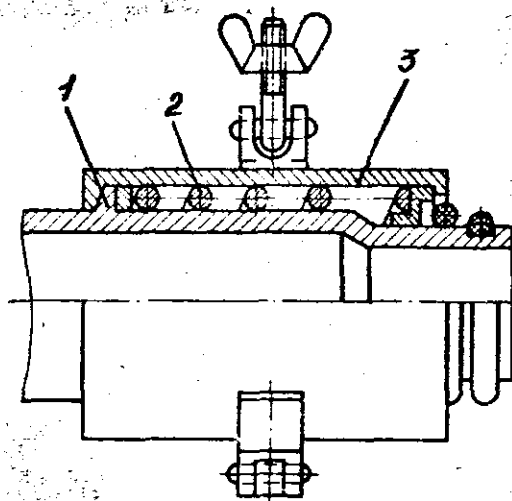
Положение приспособления для сжатия пружины при сборке кожуха рессоры КТА:
